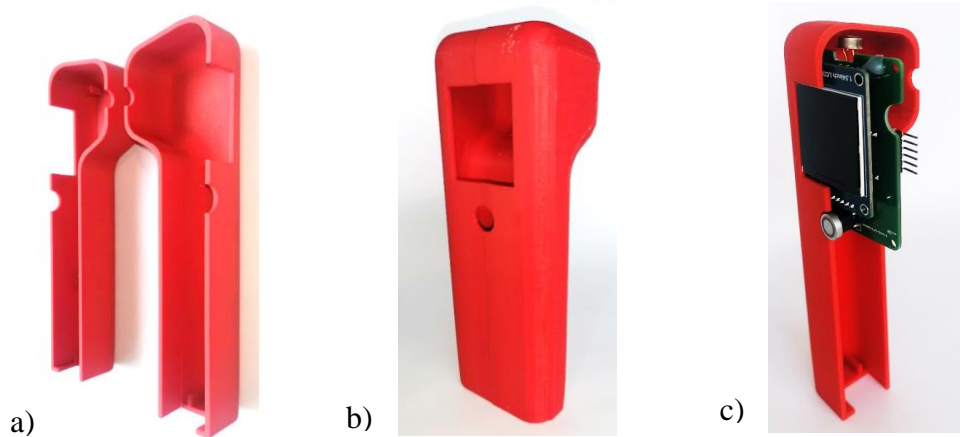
a) Componente izq. y der. de la carcasa b) Carcasa cerrada c) Componente izq. con PCB
